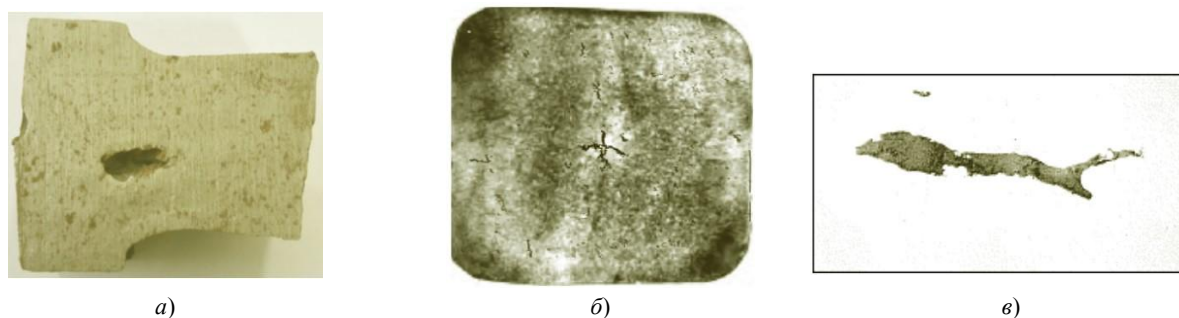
Дефекты литья в деталях подвижного состава: а — сосредоточенная усадочная раковина в литом колесном центре; б — внутренняя осевая горячая трещина в заготовке оси колесной пары; в — оксидные неметаллические включения в литевой колесной стали
